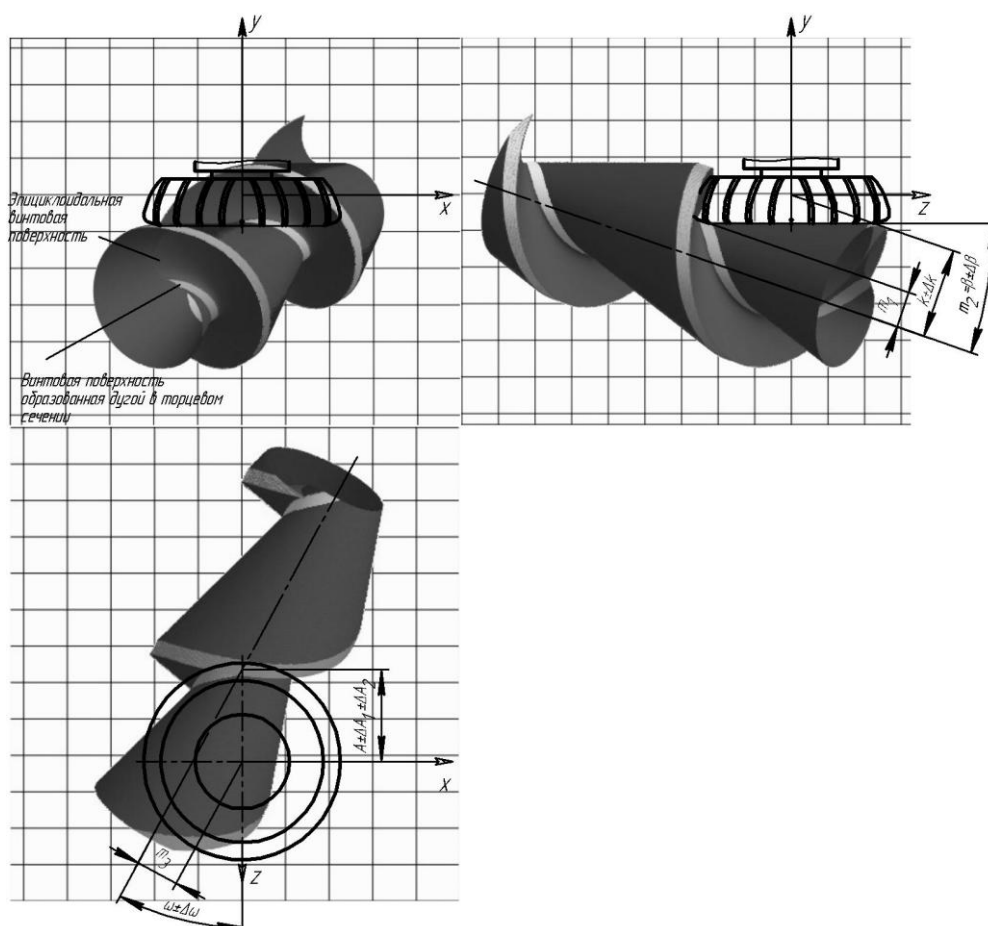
Схема установки дисковой фрезы при обработке полузакрытой винтовой поверхности
